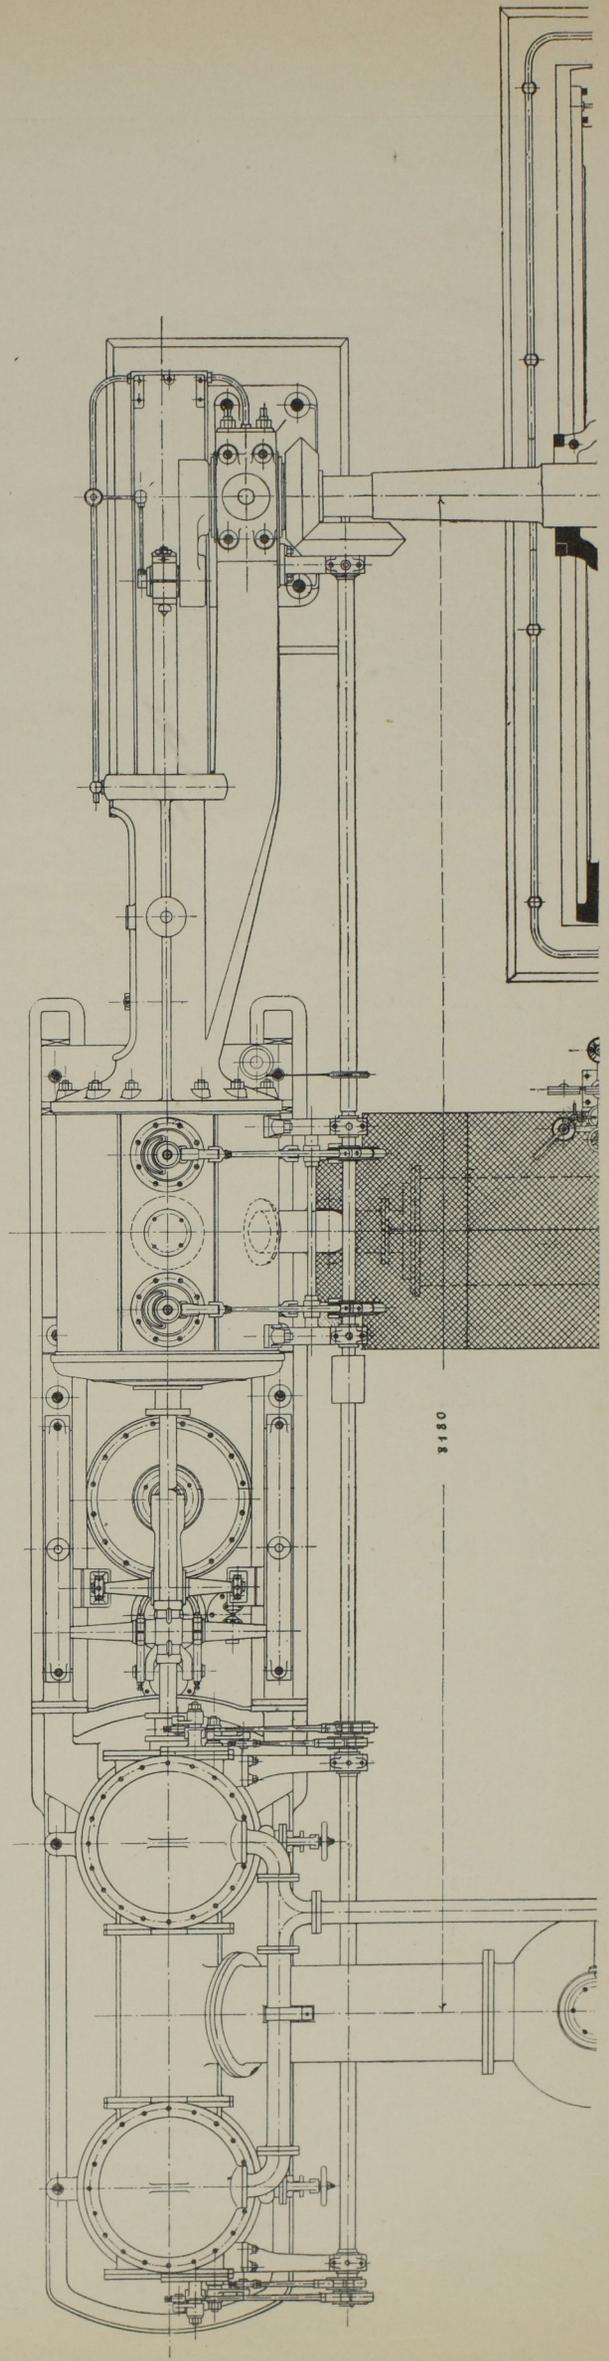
Pumpmaschine der Berliner Wasserwerke in Lichtenberg B. Grundriss der halben Pumpmaschine. Massst. 1:40.
